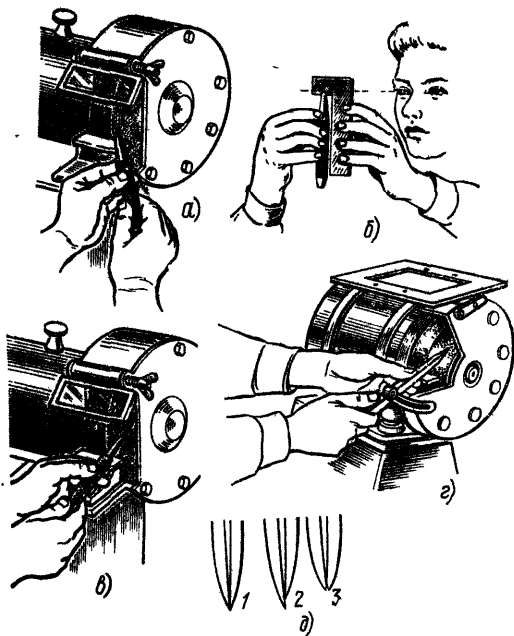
Заточка разметочного инструмента: а — заточка кернера, б — проверка угла заточки кернера по шаблону, в — заточка чертилки, г — заточка ножек разметочного циркуля, д — проверка правильности заточки: 1 — правильная заточка (концы ножек соприкасаются), 2, 3 — неправильная (ножки имеют разную длину, концы ножек не соприкасаются)
